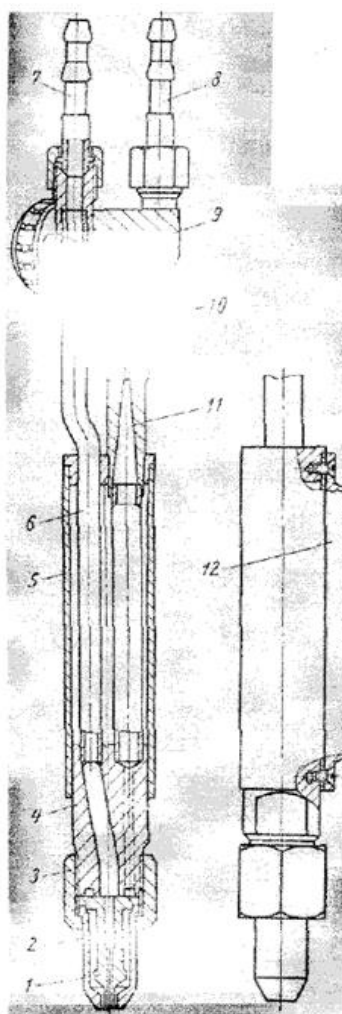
Малогабаритный двухвентильный резак газорезательной машины «Радуга»:
